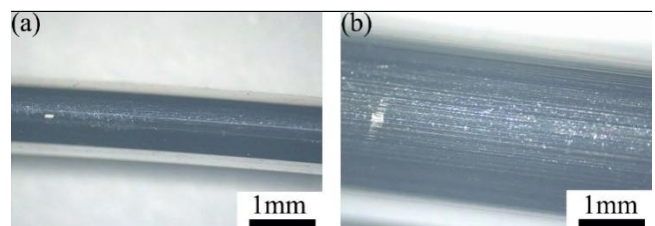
铝合金焊丝表面质量(a)MIG 焊丝(b)TIG 直条焊丝
